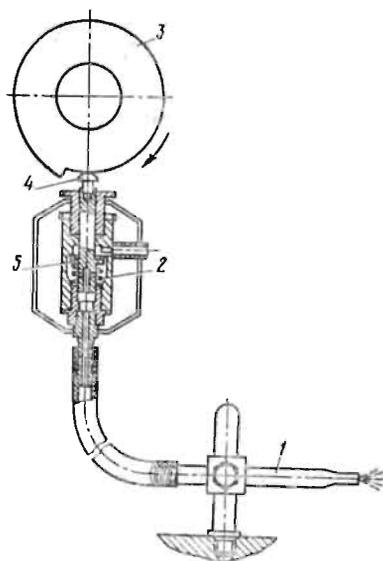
Пневматический сбрасыватель (сдуватель):
